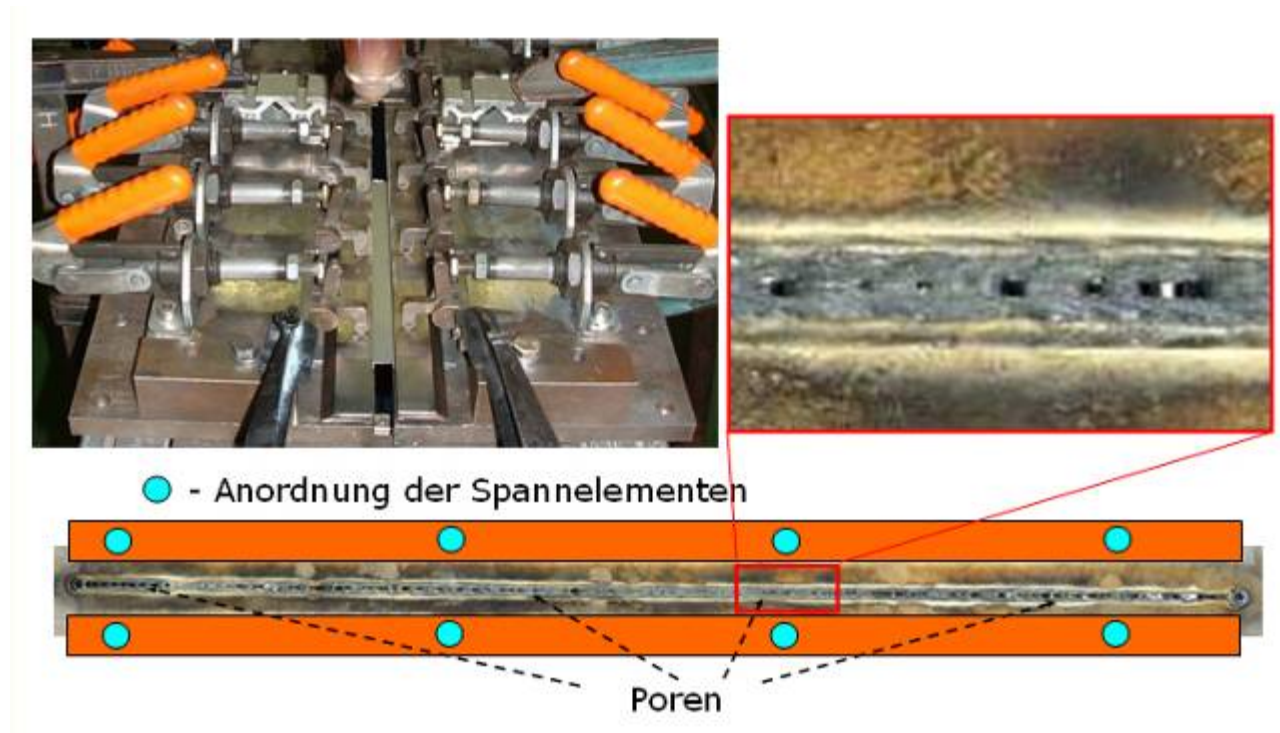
Stabile streifenförmige Spannbacken (acht Spannelemente)
